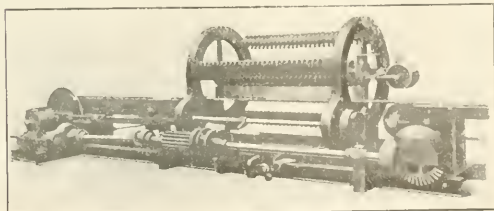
CORTADORA AUTOMÁTICA DE LADRILLOS
